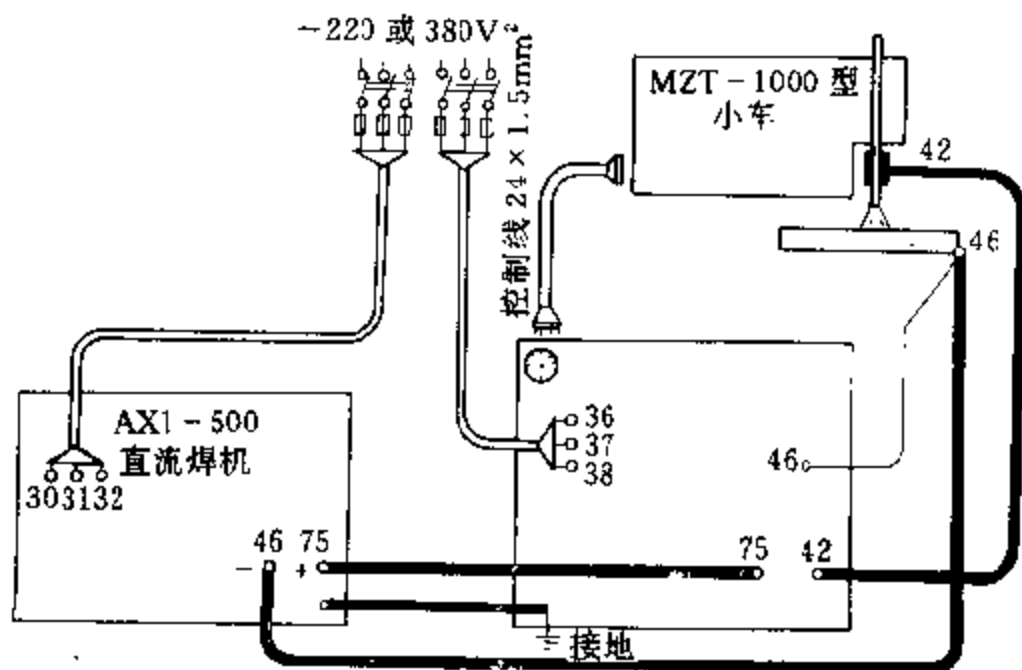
用直流电源时 MZT-1000 型焊机的外部接线图
